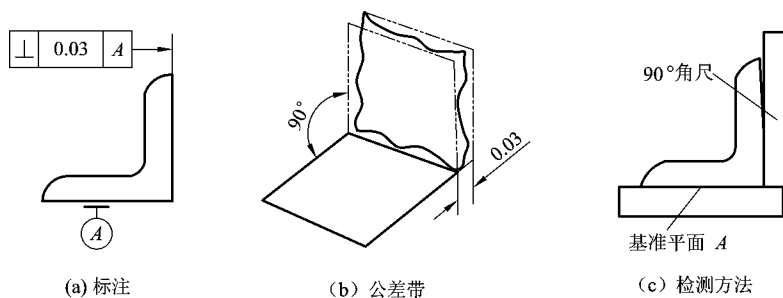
垂直度的标注、公差带及检测方法
